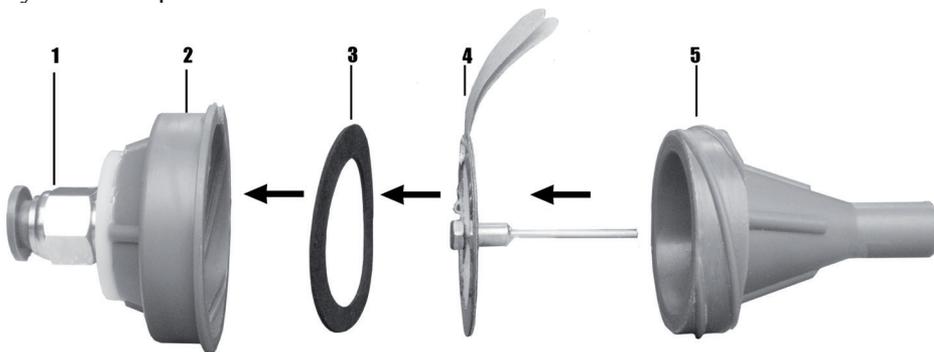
Схема сборки патрона-разбавителя пробы пыли
